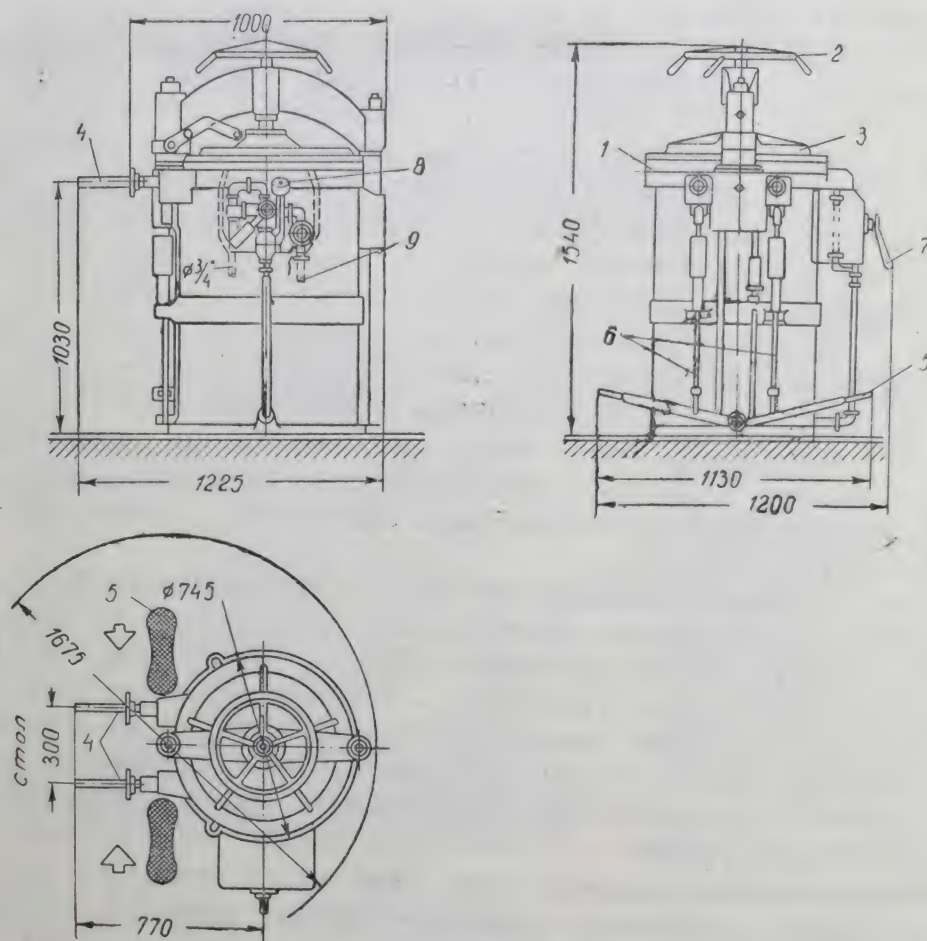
Пневматический шприц емкостью цилиндра 220 л:
